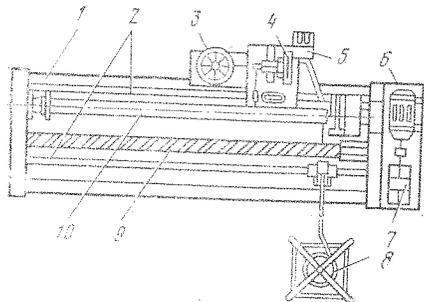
Общий вид щеткомоточного станка ЩНС:
